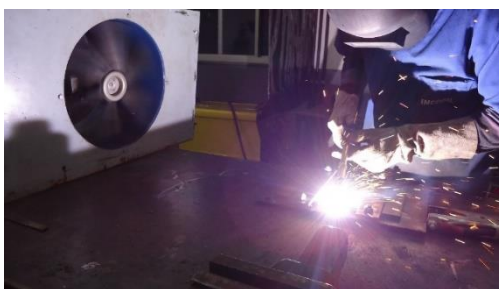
Sistema de soldagem. Corrente de ar agindo no sentido transversal ao sentido de soldagem.
